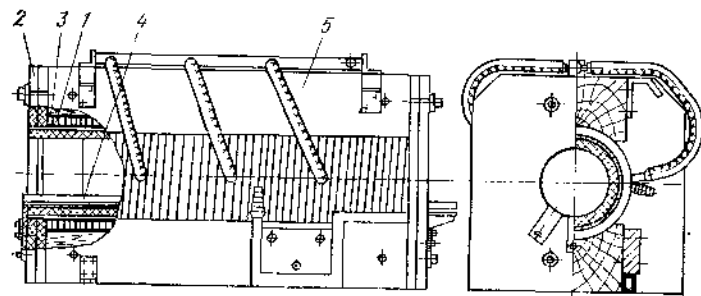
Индуктор установки для сквозного нагрева заготовок
